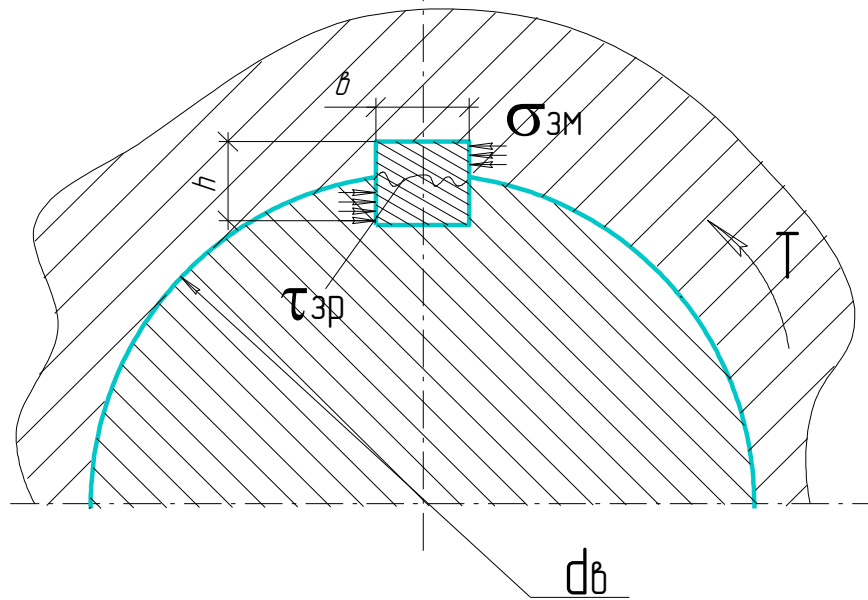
Конструктивна схема шпонкового з'єднання
